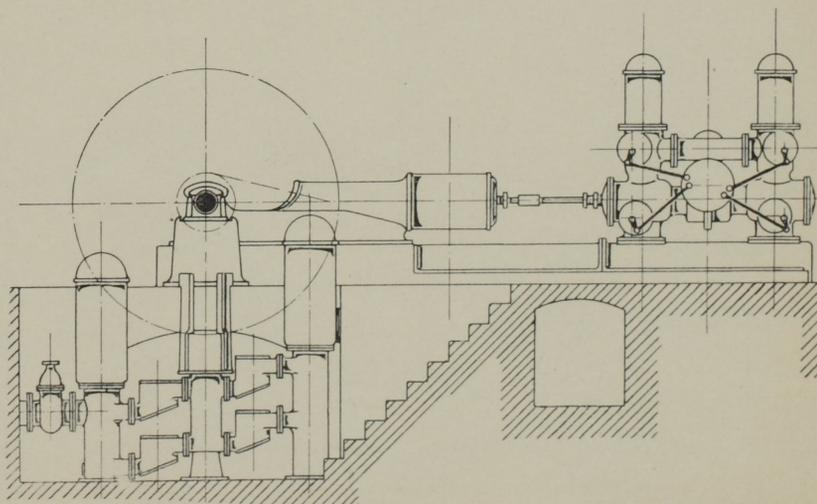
Seitenansicht der Druck- und Zubringepumpen. Masst. 1:75.
